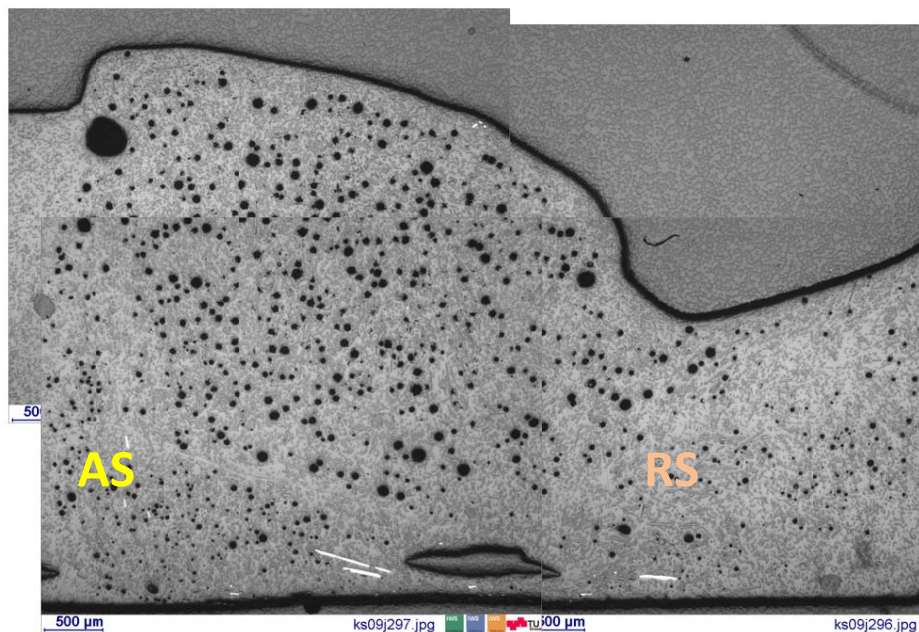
Schweißnahtquerschnitt beheizter Pinstift KS_0906_S016
